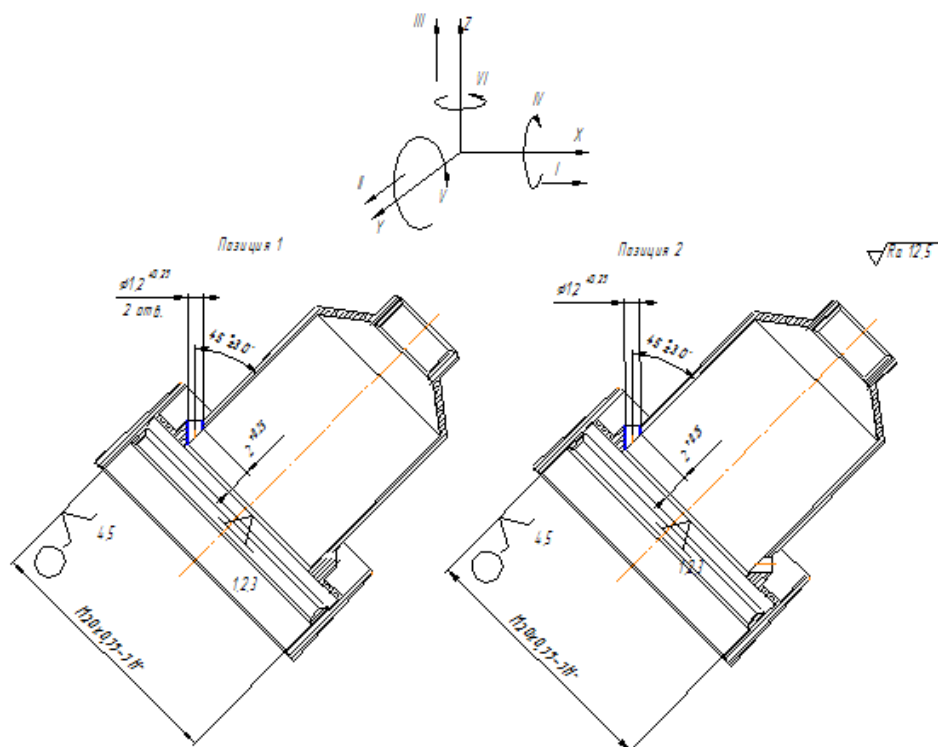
Схема базування на 035 операції Фрезерній з ЧПК
